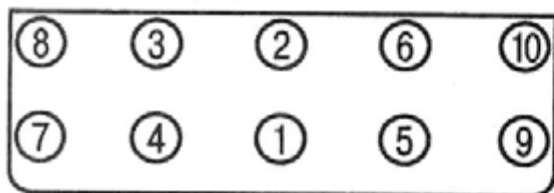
Последовательность затяжки гаек крепления головки блока цилиндров
